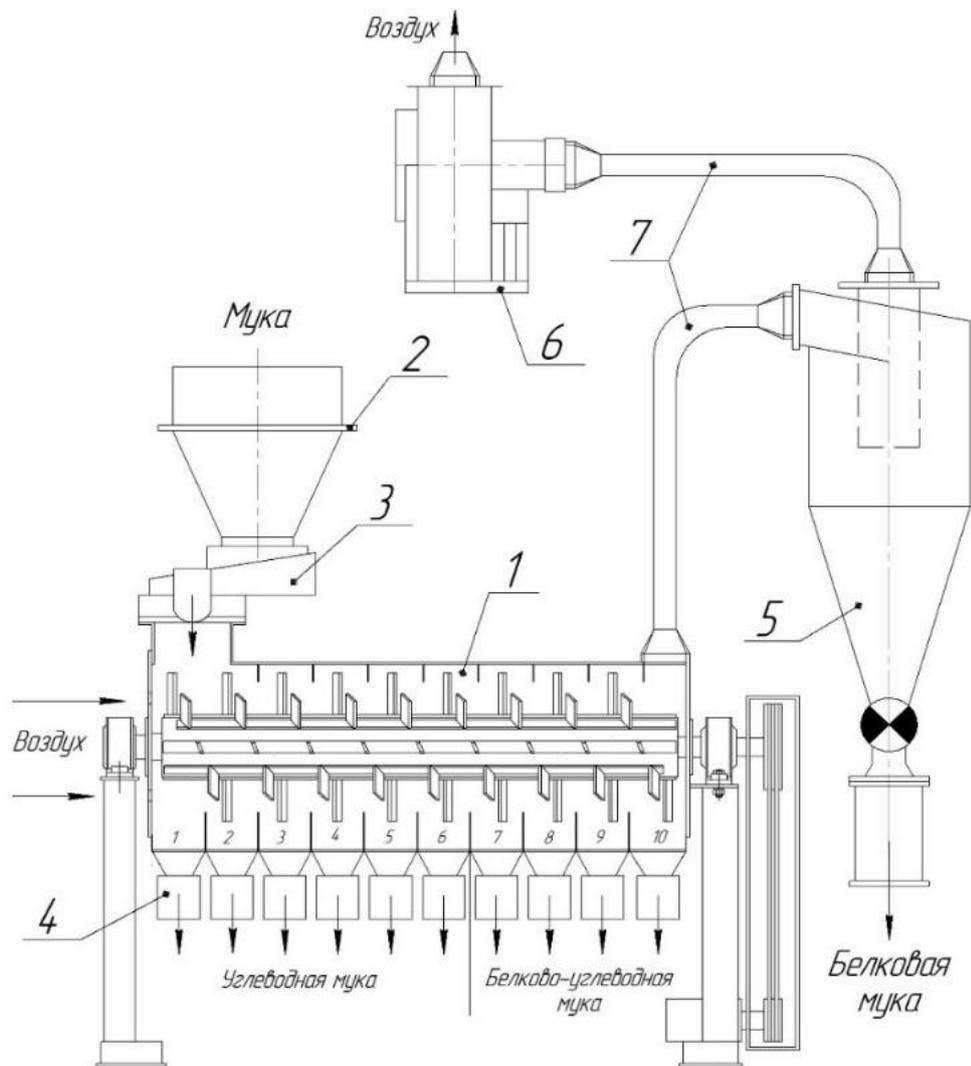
Установка центробежно-роторного пневмокласификатора
